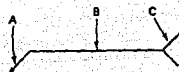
Simbología en soldadura. A) establece la localización de la soldadura. B) contiene los símbolos de soldadura. Si el símbolo se encuentra debajo de la línea de referencia, quiere decir al "lado de la flecha". Los símbolos situados arriba de la línea de referencia son para el "otro lado". C) la sección de cola, cuando se utiliza, contiene la especificación, proceso u otra información.
